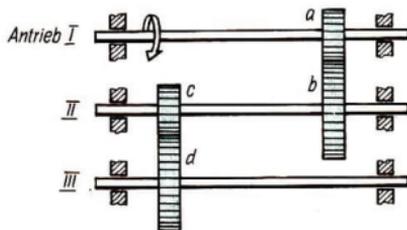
/1 Zahnradgetriebe einer Verpackungsmaschine
